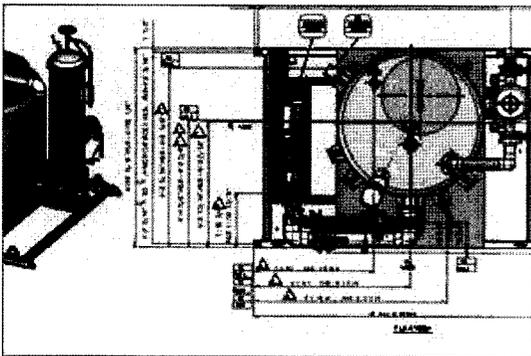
SolidWorks의 eDrawing (<http://www.solidworks.com/pages/products/edrawings/eDrawings.html>)
